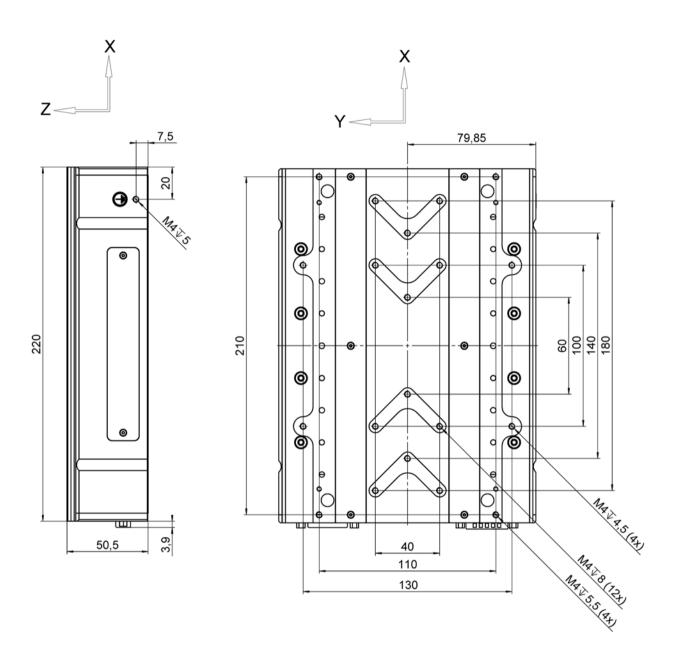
Abmessungen des V-551.2D: Seitenansicht und Draufsicht
